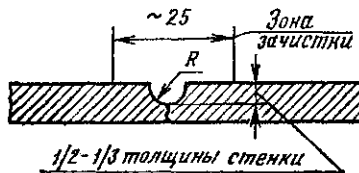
Профиль канавки вдоль трещины, подготовленной под заварку
